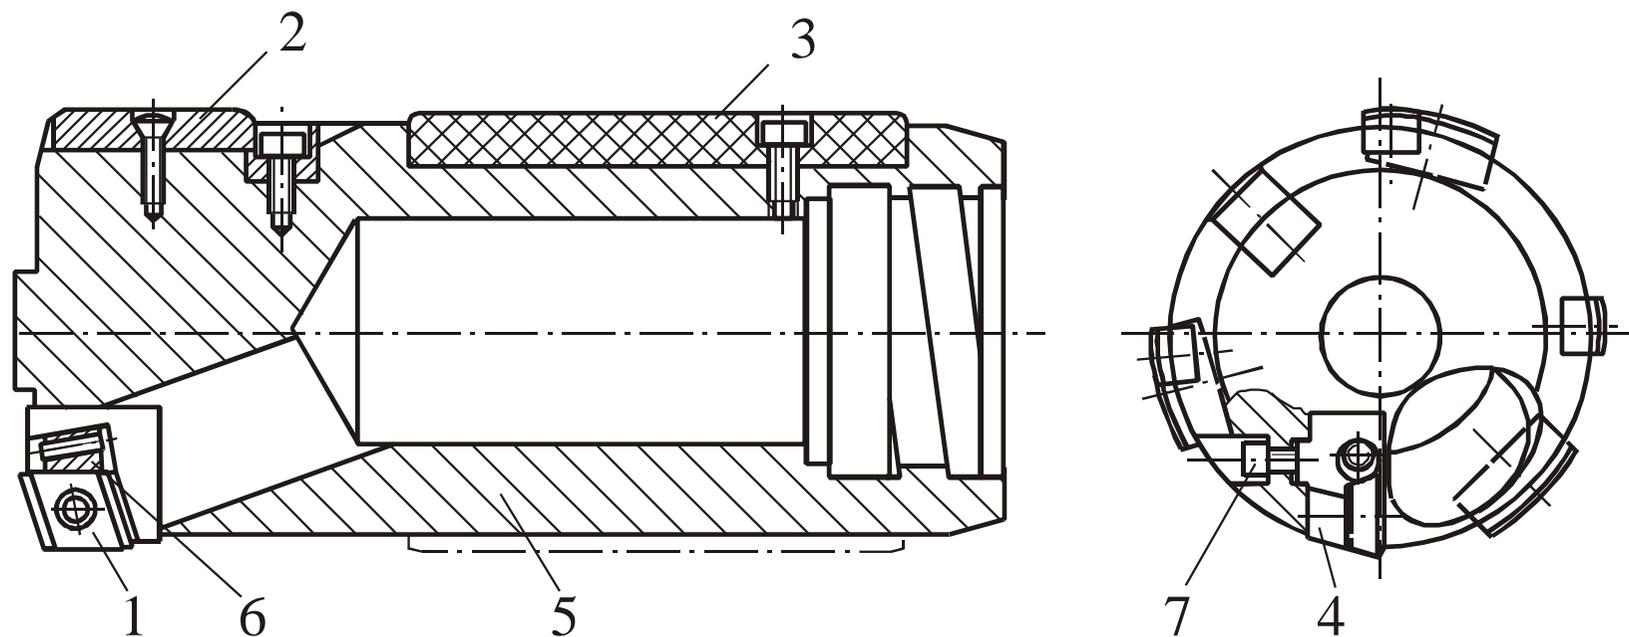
Расточная головка фирмы «Votek» (Германия) для обработки глубоких отверстий: 1 – твердосплавная режущая пластина; 2 – твердосплавная направляющая; 3 – пластмассовая направляющая; 4 – кассета; 5 – корпус головки; 6 – клин; 7 – винт
